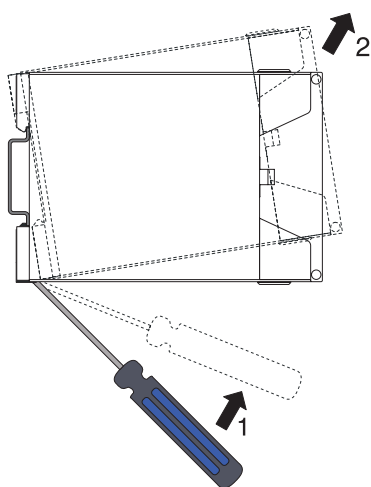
Демонтаж барьеров с DIN-рейки
